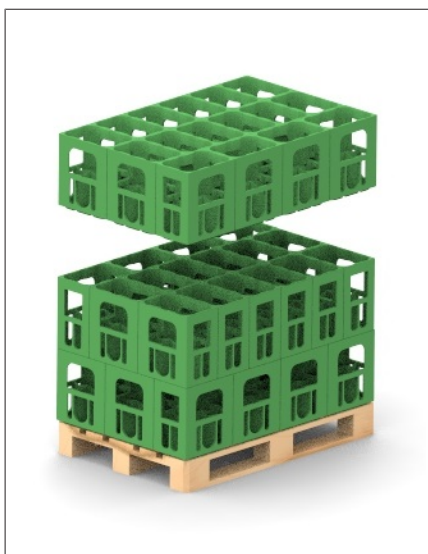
Empilhamento em conjunto de 180° sobre o palete
